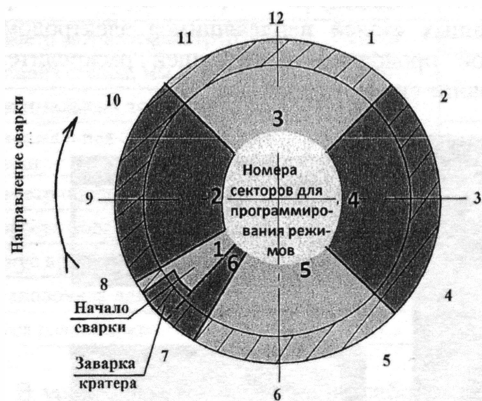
Схема разбиения периметра сварного соединения на сектора в часовых координатах для программирования процесса сварки
